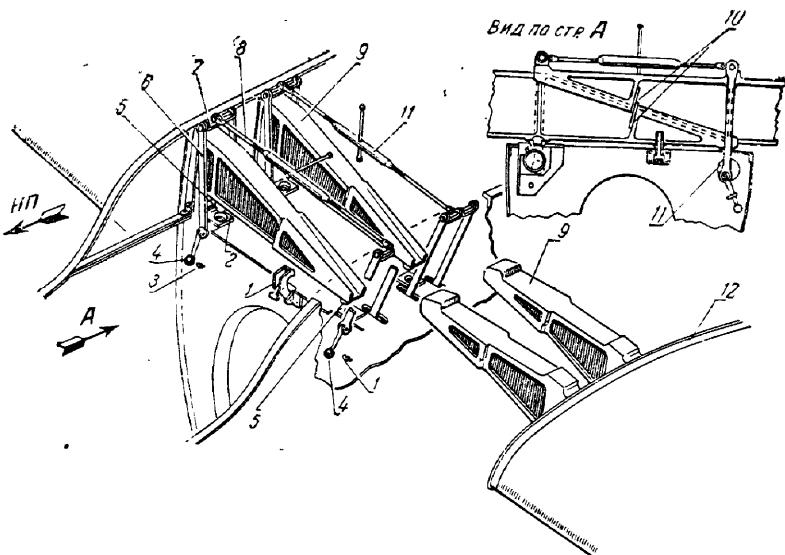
Планеры А-11 и А-13. Схемастыковки крыла
